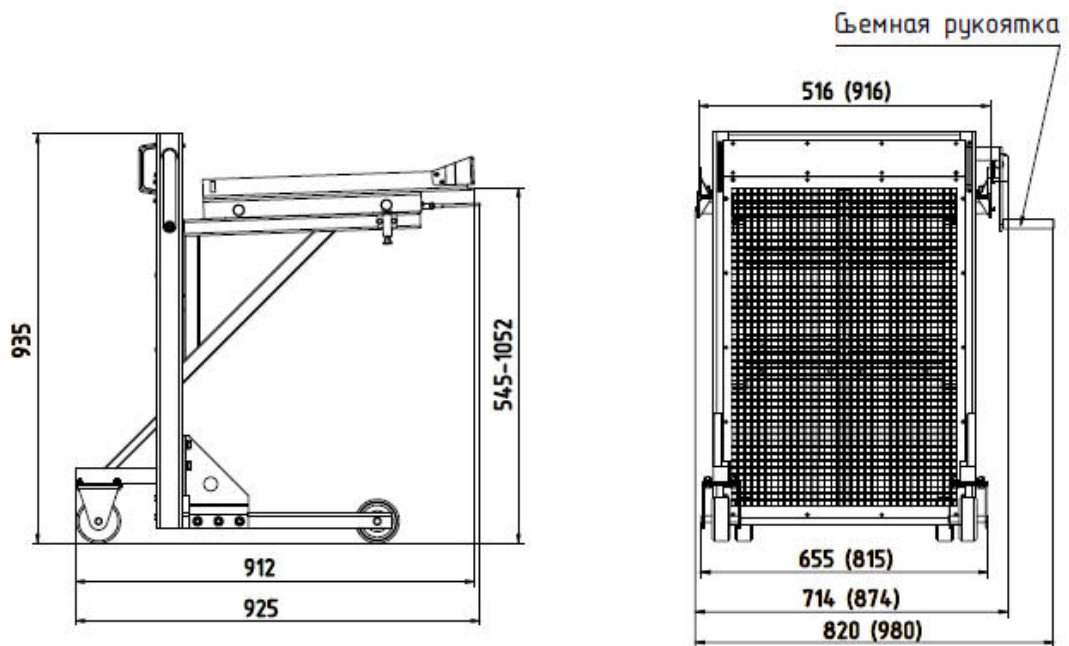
Общий вид и габаритные размеры сервисной тележки
